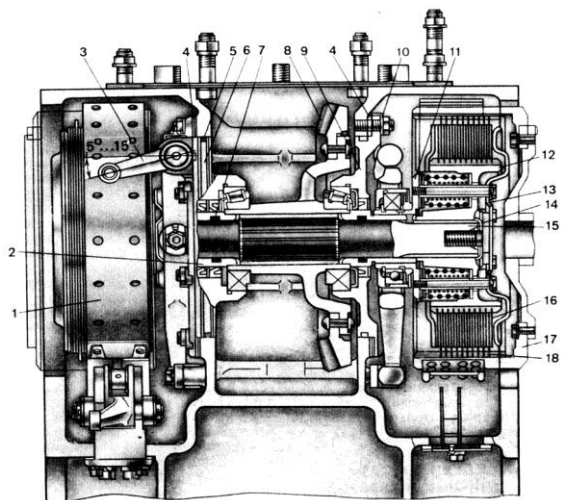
Задний мост трактора Т-70С: 1 - тормозная лента; 2 - распорная втулка; 3 - рычаг муфты поворота; 4 - регулировочные прокладки; 5 и 7 — уплотнительные кольца; 6 - левый стакан подшипника; 8 - ведомое зубчатое колесо главной передачи; 9 - правый стакан подшипника; 10 - стопорная шайба; 11 - отжимной диск; 12 - ведущий барабан муфты поворота; 13 - нажимной диск; 14 - стопорная шайба; 15 - вал заднего моста; 16 - ведущий диск; 17 - ведомый барабан муфты поворота; 18 - ведомый диск
